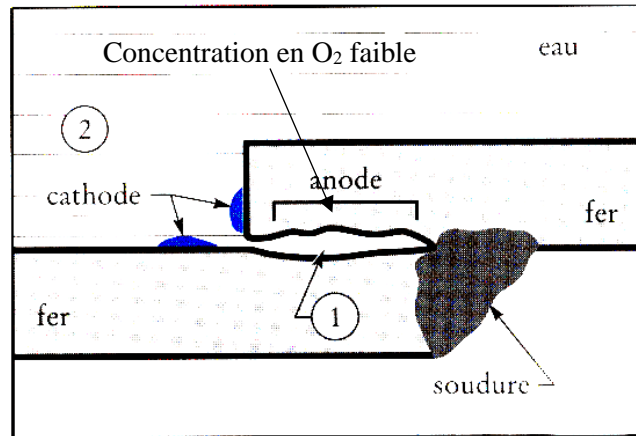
Corrosion caverneuse à l'interface d'un assemblage soudé.
